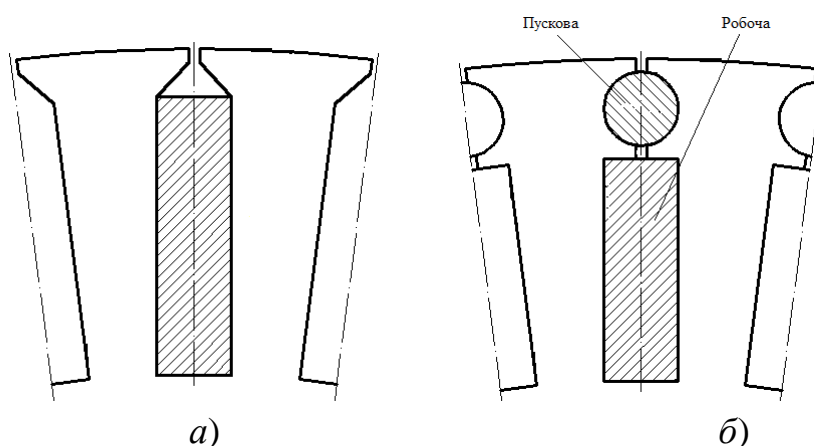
Форми пазів для першої та другої конструкції КЗ обмотки ротора
